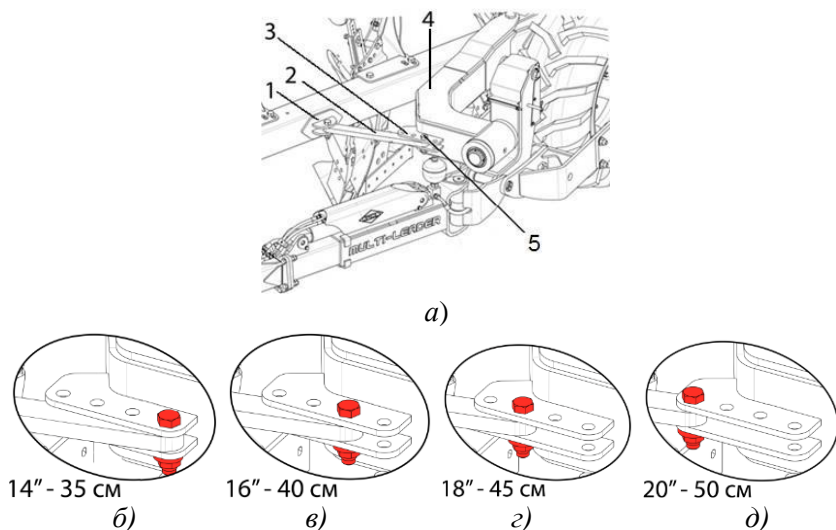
Схема установки тяги регулирования положения опорного колеса при выборе ширины захвата корпуса плуга:
